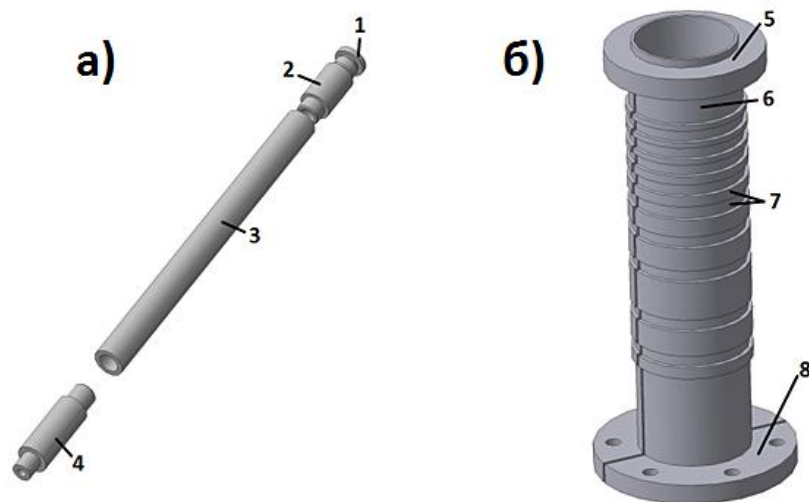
Тигель (а) и нагреватель (б) ростовой установки. а) Тигель состоит из: 1) крышка, 2) контейнер для загрузки тефлона, 3) контейнер для загрузки шихты, 4) ножка. б) конструкция резистивного нагревателя: 5) площадка для экрана, 6) нагреватель, 7) стенка с переменной толщиной для обеспечения необходимого температурного поля, 8) площадка контакта с тоководом.
